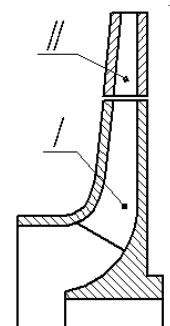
Ескіз контрроторного ступеня I – робоче колесо; II – лопатевий диск.
